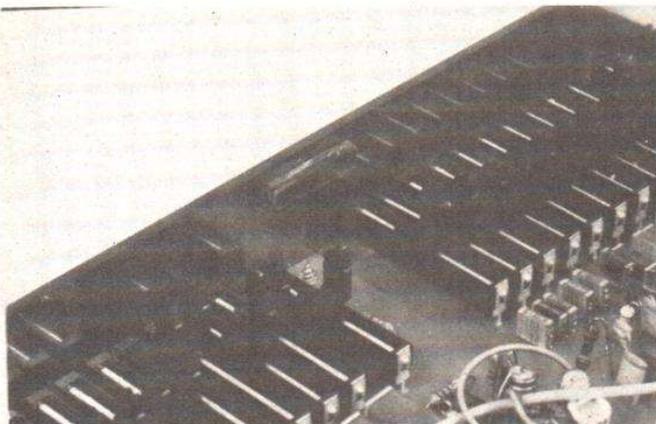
L'alignement des potentiomètres. Sur la façade, une pièce rapportée guide le dessus du capot.
